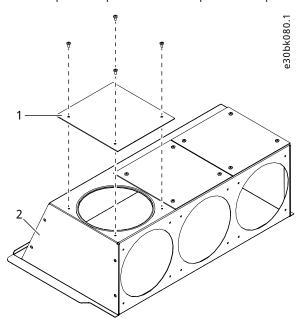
Instalação da chapa de tampa do opcional de resfriamento do canal traseiro
